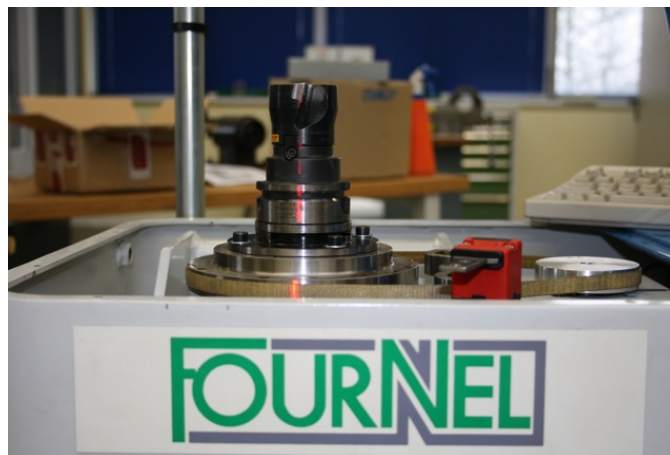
Vue de l'ensemble « outil – porte outil ».
